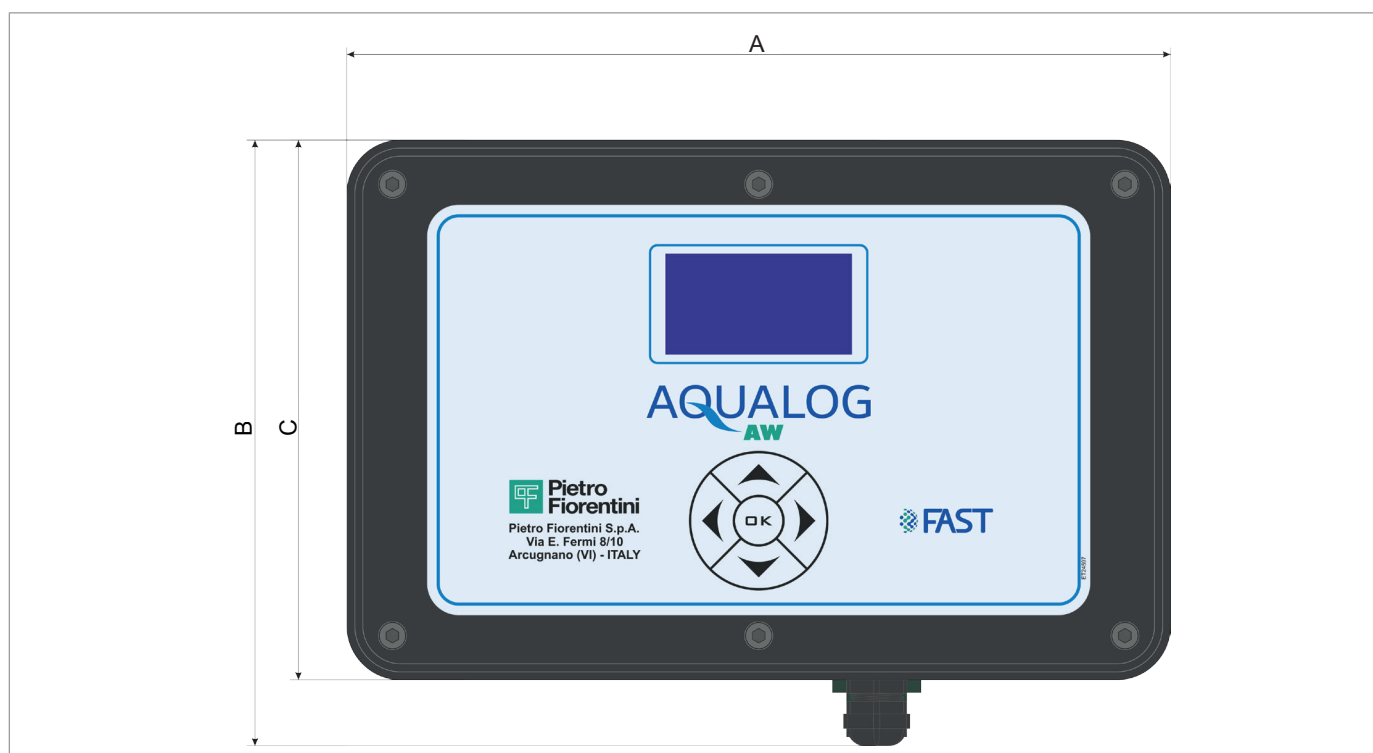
Dimensioni AQUALOG AW versione connettore MIL, vista frontale
